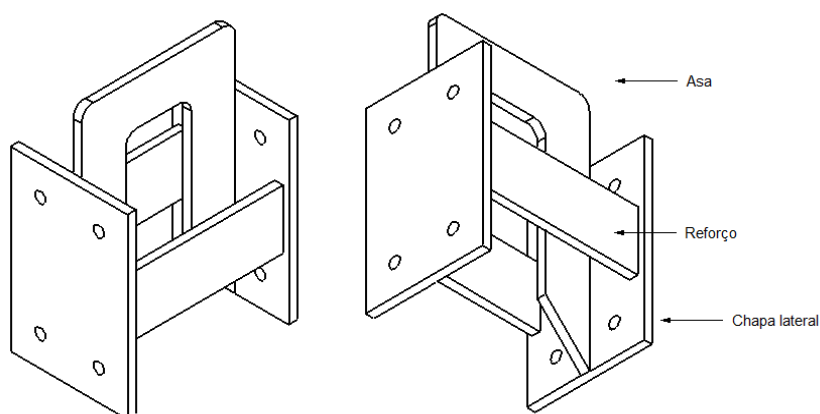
Perspectiva geral dos olhais de suspensão das vigas superiores
